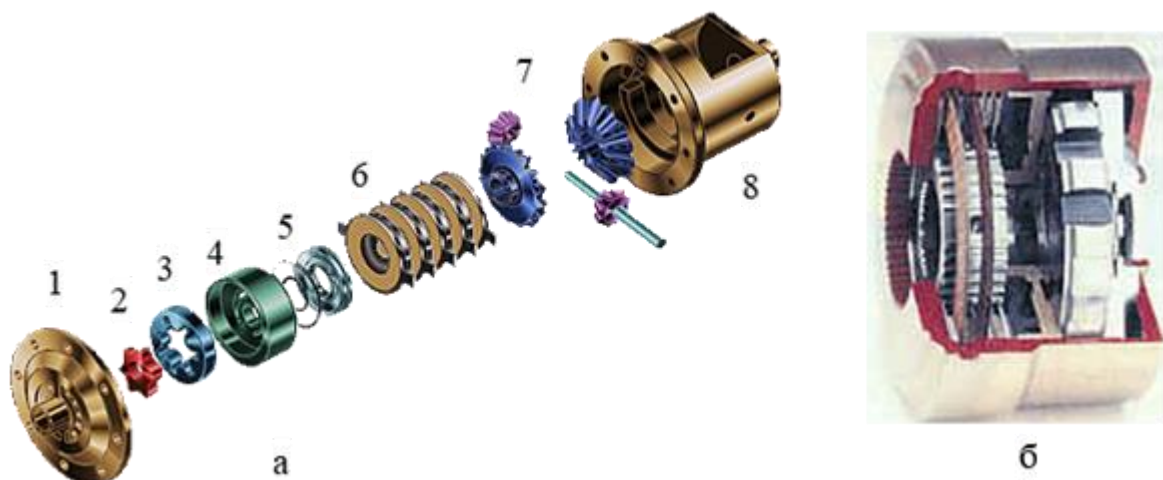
Героїдна муфта: а – устрій; б – загальний вигляд узборі
